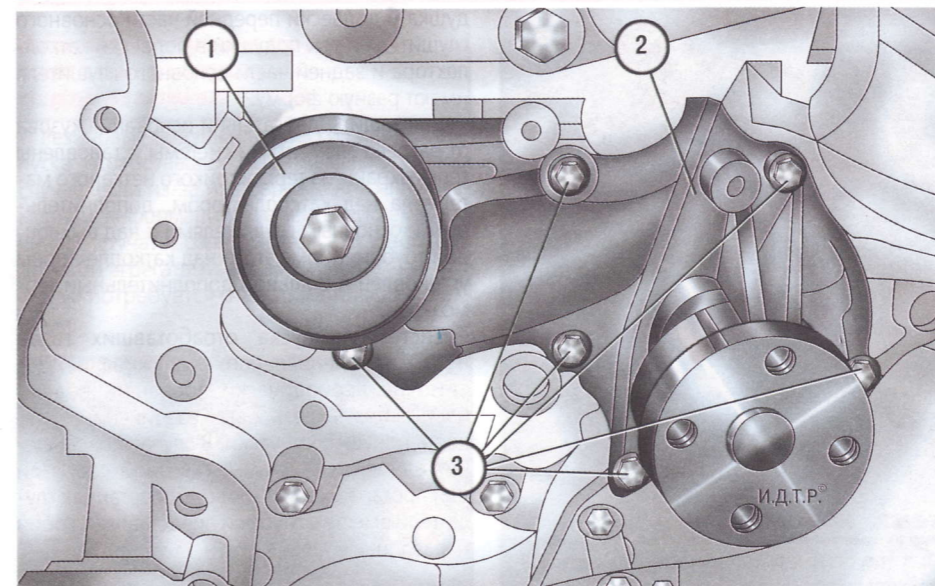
Водяной насос: 1 – натяжной ролик ремня привода газораспределительного механизма; 2 – водяной насос; 3 – болты крепления водяного насоса к блоку цилиндров двигателя; 4 – болт крепления натяжного ролика к корпусу водяного насоса
